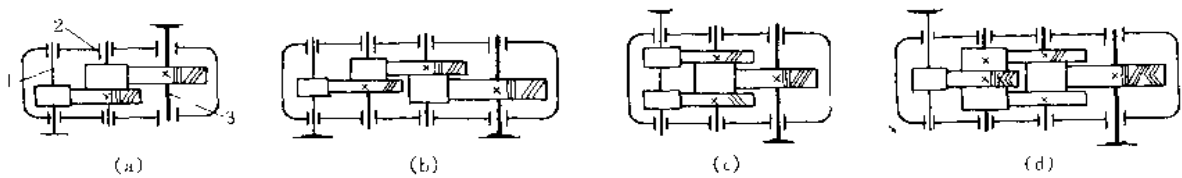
二级圆柱齿轮减速器齿轮布置
